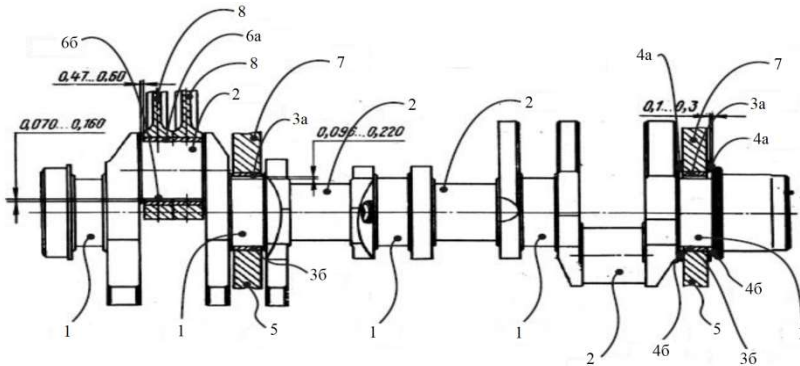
Зазоры в подшипниках коленчатого вала двигателя (1 – коренная шейка; 2 – шатунная шейка; 3а; 3б – вкладыш верхний и нижний коренного подшипника; 4а; 4б – полукольца коленчатого вала; 5 – крышка коренного подшипника коленчатого вала; 6а; 6б – шатунные вкладыши верхние и нижние; 7 – постель на блоке цилиндров; 8 – шатун в сборе)
